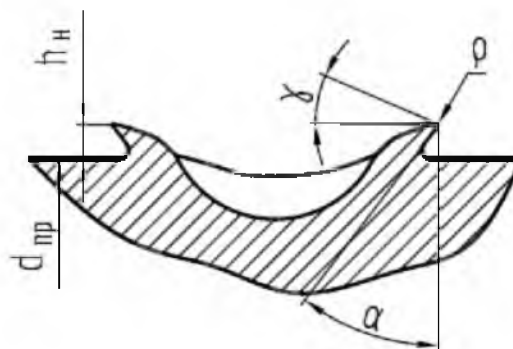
Схема наплывов металла, формируемых на поверхности проволочного инструмента в процессе ЭКО
